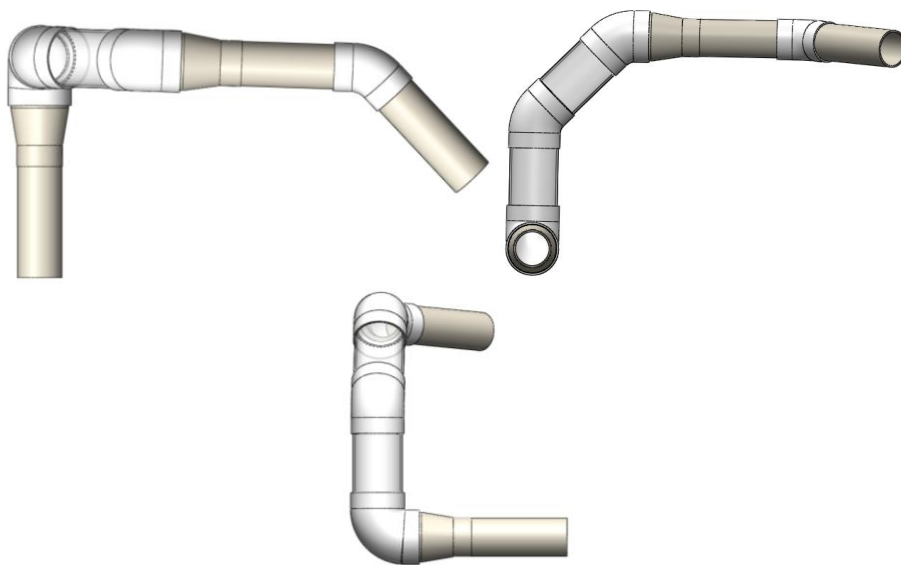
Diseño CAD de la maqueta. (Vistas: Superior, Frontal y Lateral Izquierda).
